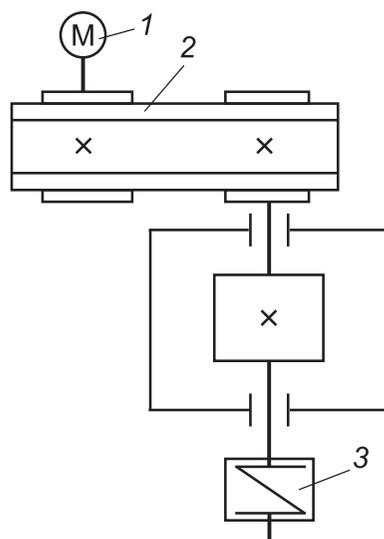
Кинематическая схема: 1 – двигатель; 2 – передаточный механизм; 3 – рабочий орган
